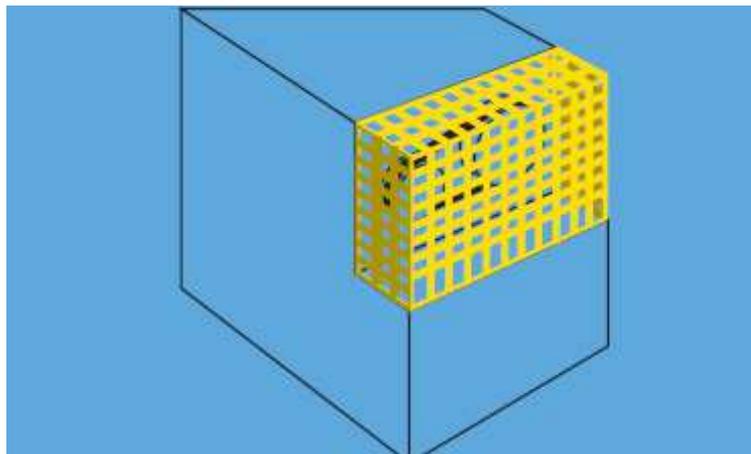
Protección permanente contra accesos mediante guardas de aislamiento fijas
